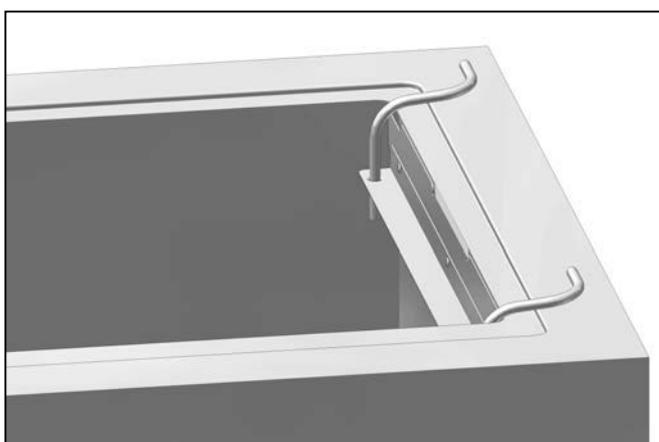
Fixation de la barrette à tubes sur la cuve du bain
